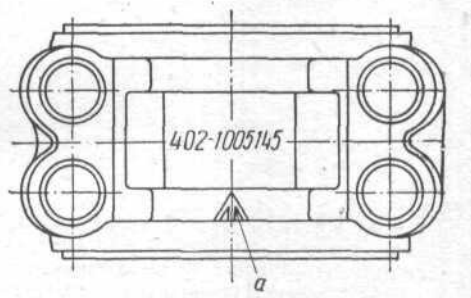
Крышка среднего коренного подшипника коленчатого вала
